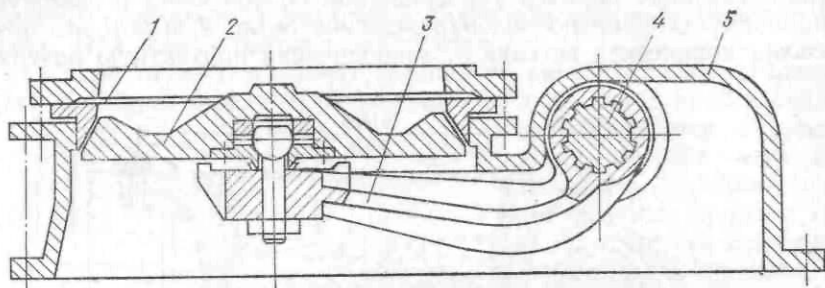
Газоуплотнительный клапан диаметром 900 мм, применяемый в клапано-конусном загрузочном устройстве конструкции ПО «Ждановтяжмаш» и ДЗМО:
